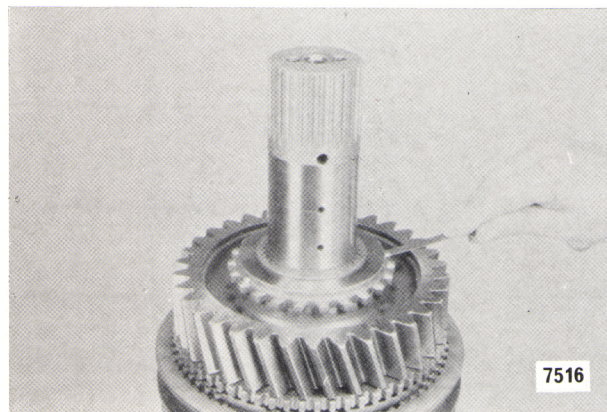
Verificando el juego axial del engranaje de 2ª velocidad
